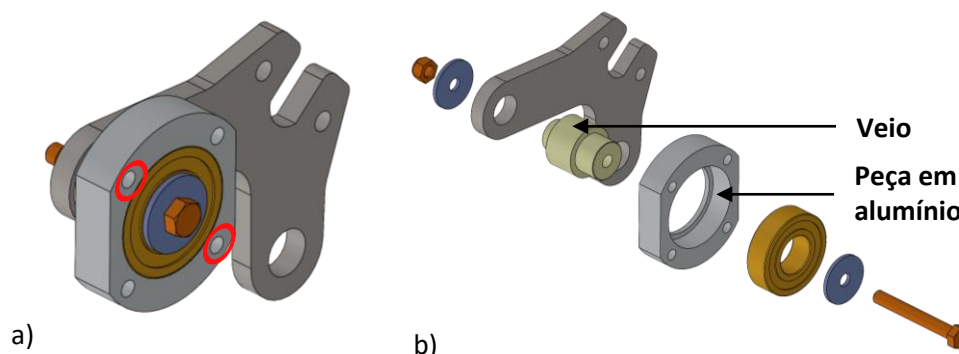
a) Ligação do braço com a estrutura superior; b) Vista explodida
